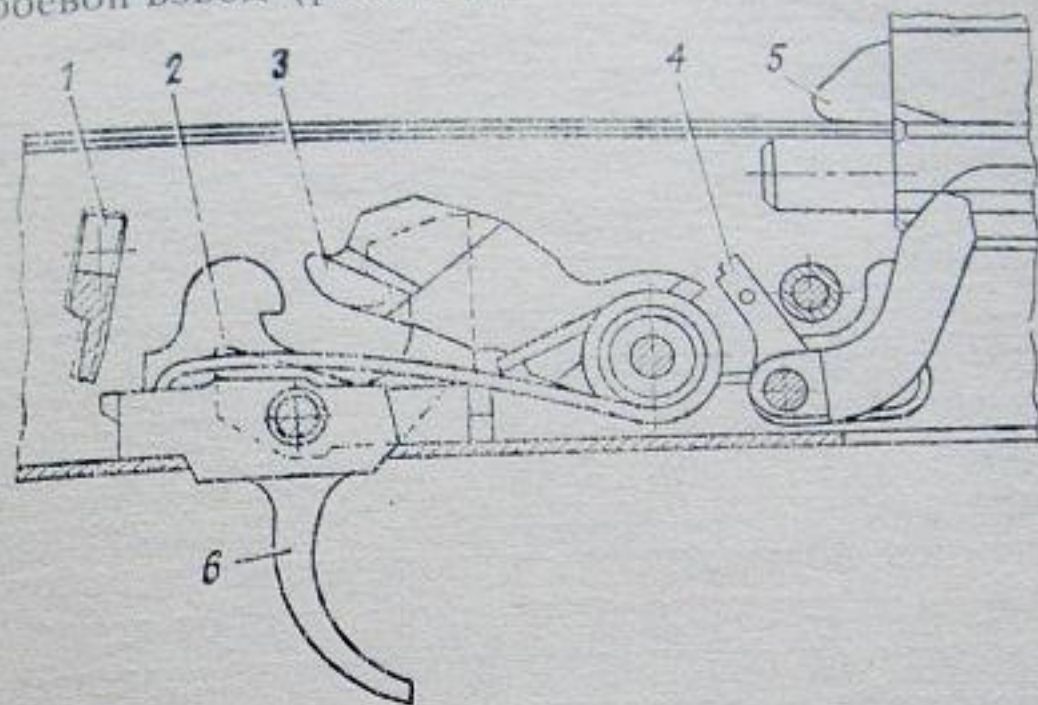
Положение частей ударно-спускового механизма перед выстрелом:
